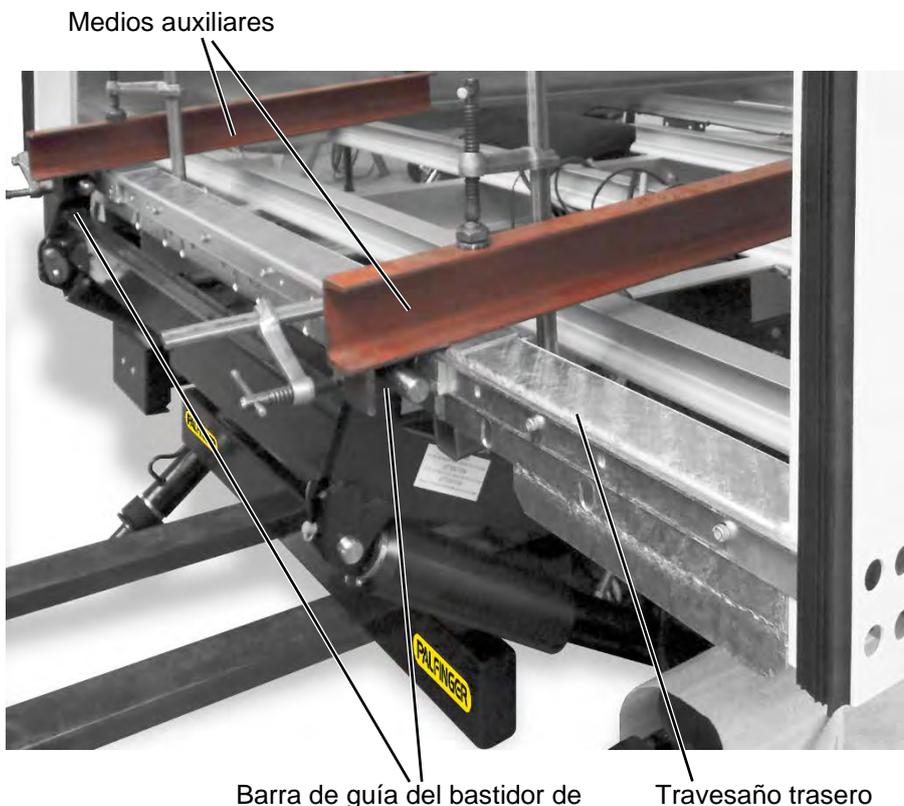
Empernar el mecanismo de elevación y los elementos auxiliares de montaje
